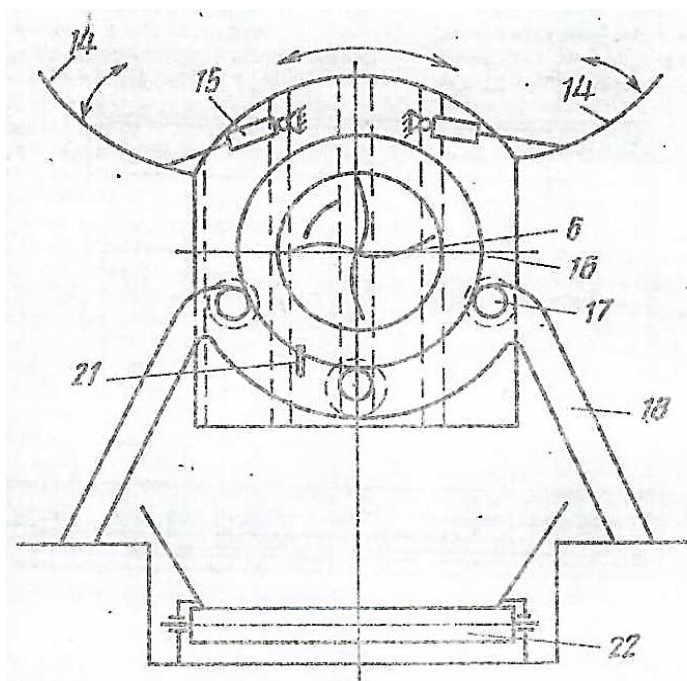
Пристрій для сушки [9], вид збоку
